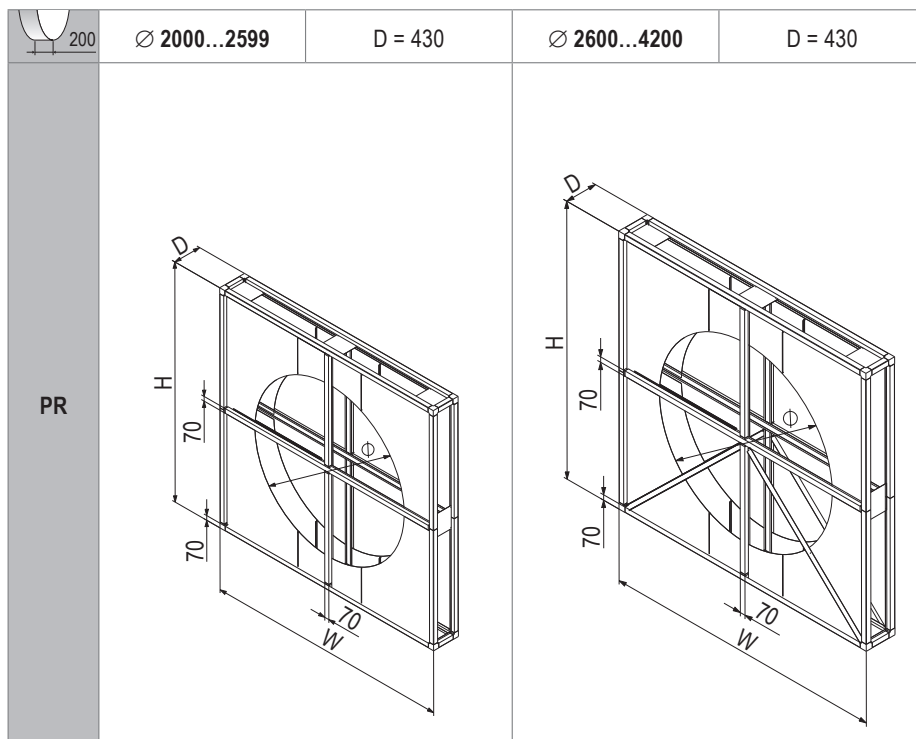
Massblatt für PR Gehäuse (Abmessungen in mm)
